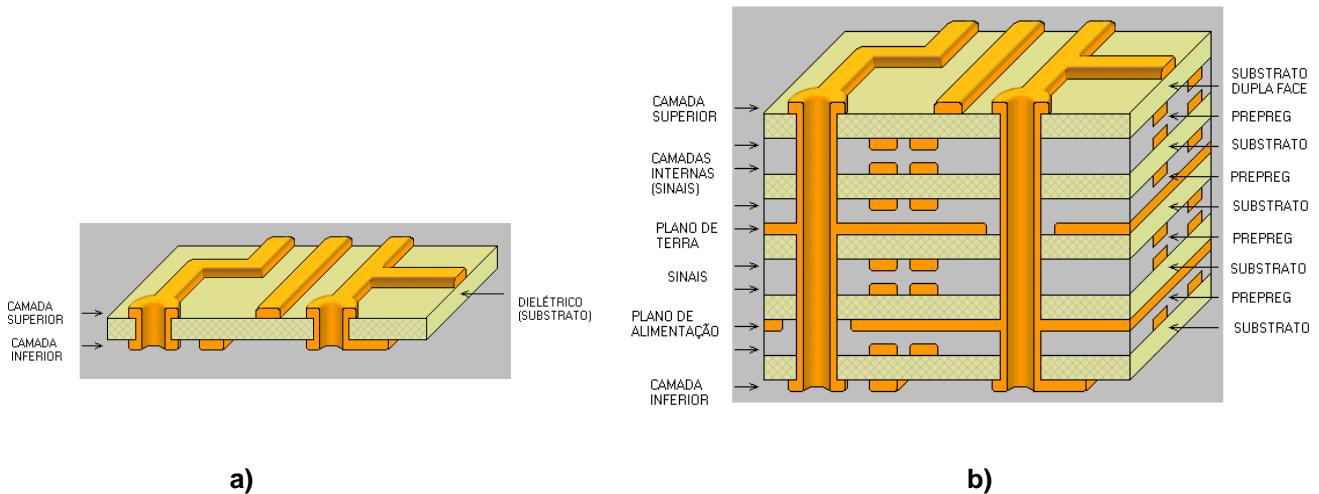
a) – Placa face dupla, b) Placa Multicamadas
